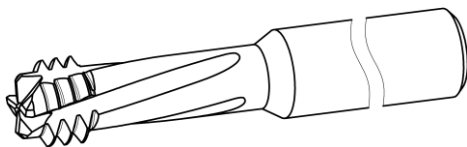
Резьбовая фреза для обработки в глухом материале
